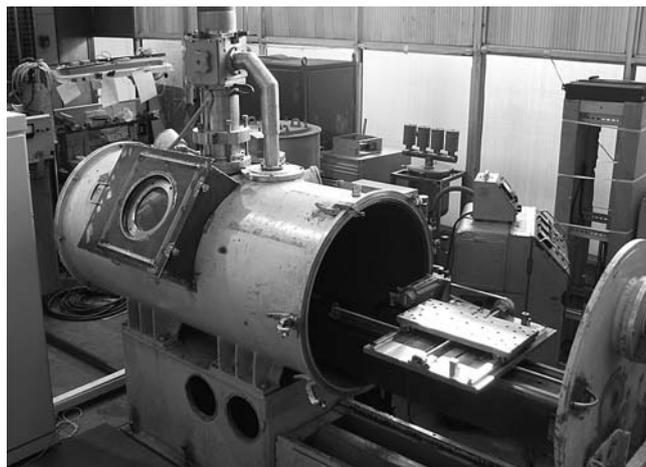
Установка электронно-лучевой сварки ЭЛУ-5
